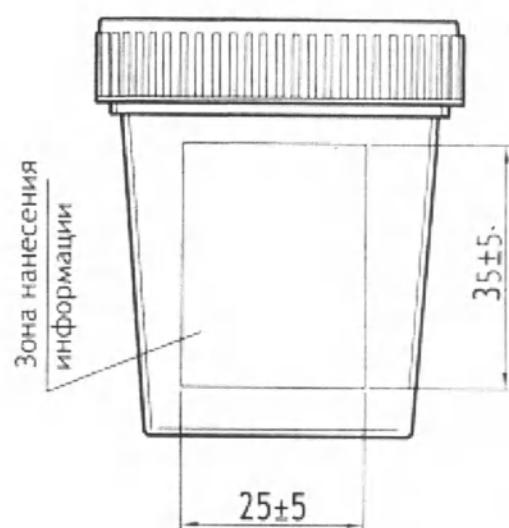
Контейнер для биопроб 60мл полимерный
